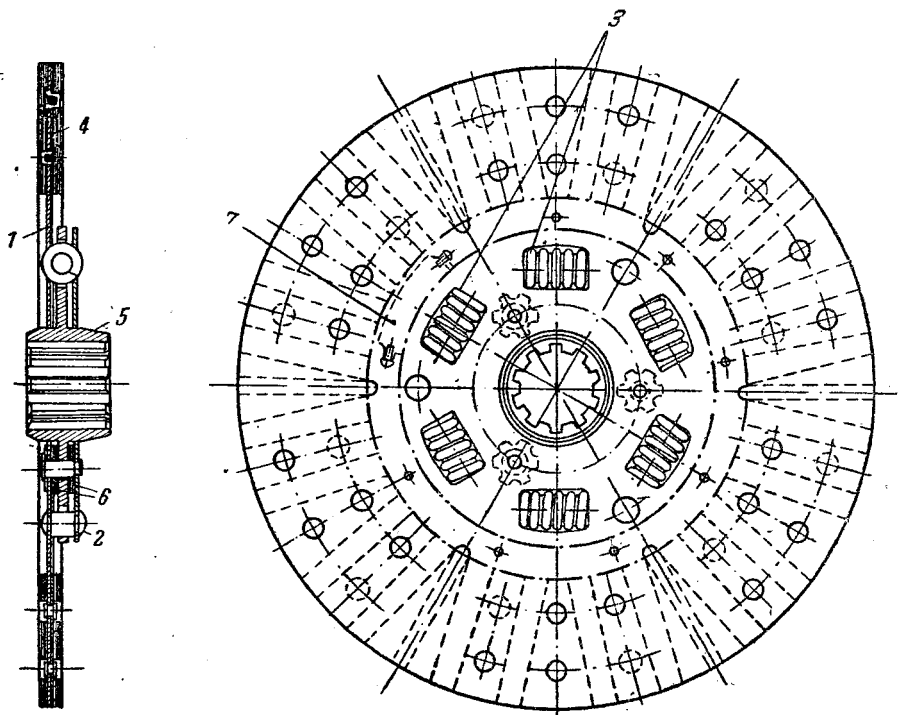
Ведомый диск сцепления шестицилиндрового двигателя.
